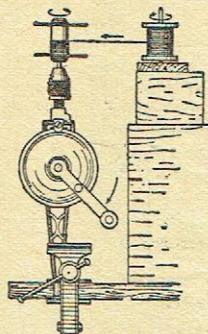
Comment s'y prendre pour exécuter le bobinage à la chignole.
